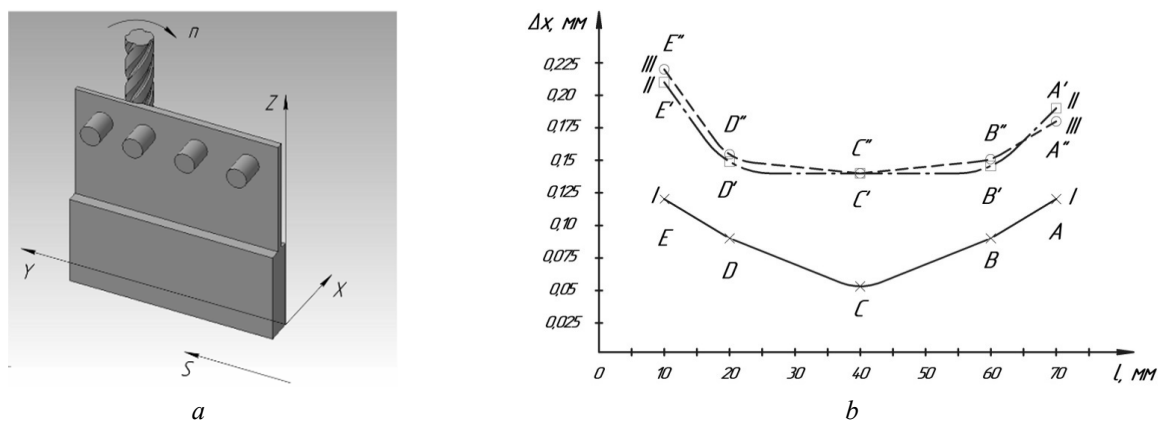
Схема фрезерования (*a*) и отклонение формы поверхности обработанной детали в сечениях I-I, II-II, III-II (*b*) с применением вспомогательного опорного модуля из 4 опор
